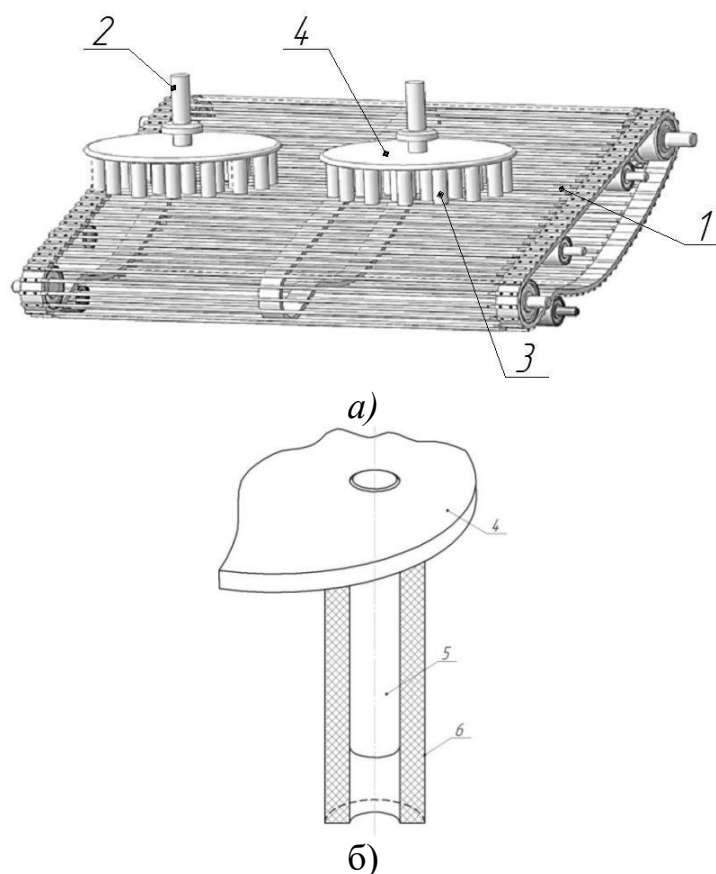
Сепаруючий елеватор із дисковими зворушувачами: а) вигляд загальний, б) робочий елемент (палець) дискового зворушувача: 1 – сепарувальний елеватор, 2 – дисковий зворушувач; 3 – палець; 4 – прогумований диск; 5 – металевий стрижень; 6 – полімерна трубка.
